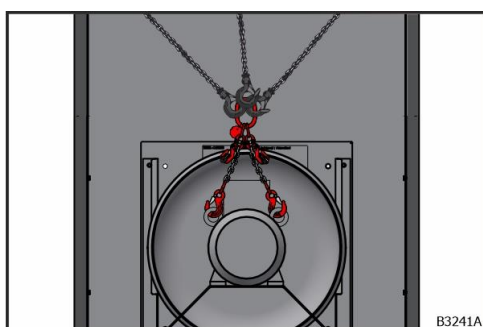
Oběžné kolo s polyesterovou smyčkou
